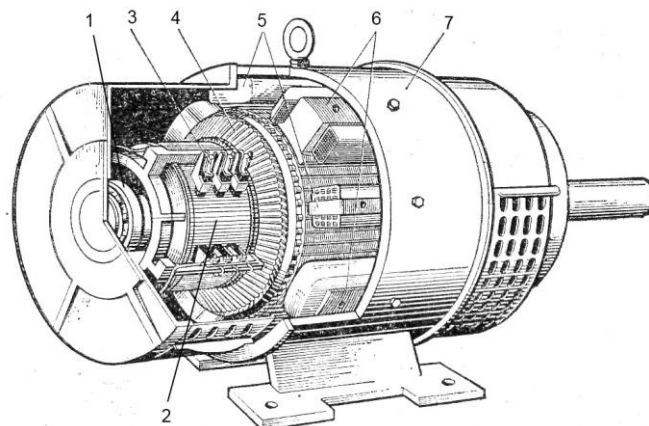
ДПТ: 1 - подшипник, 2 - коллектор, 3 - щетки 4 - якорь 5 - дополнительные полюса, 6 - обмотка возбуждения, 7- станина
